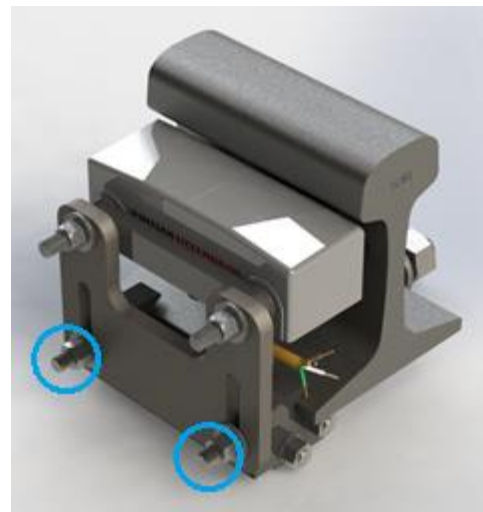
Frontansicht Radsensor Befestigungsplatte
